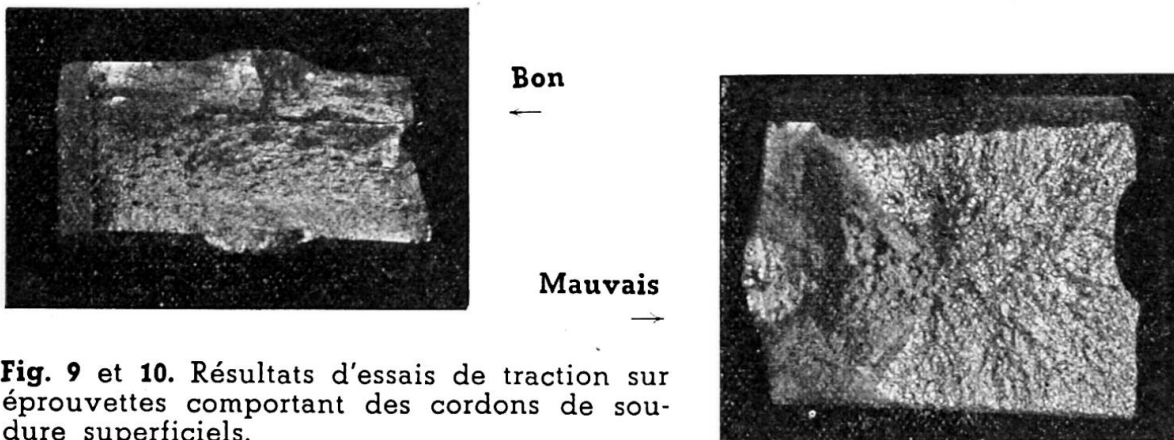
et 10. Résultats d'essais de traction sur éprouvettes comportant des cordons de soudure superficiels.
